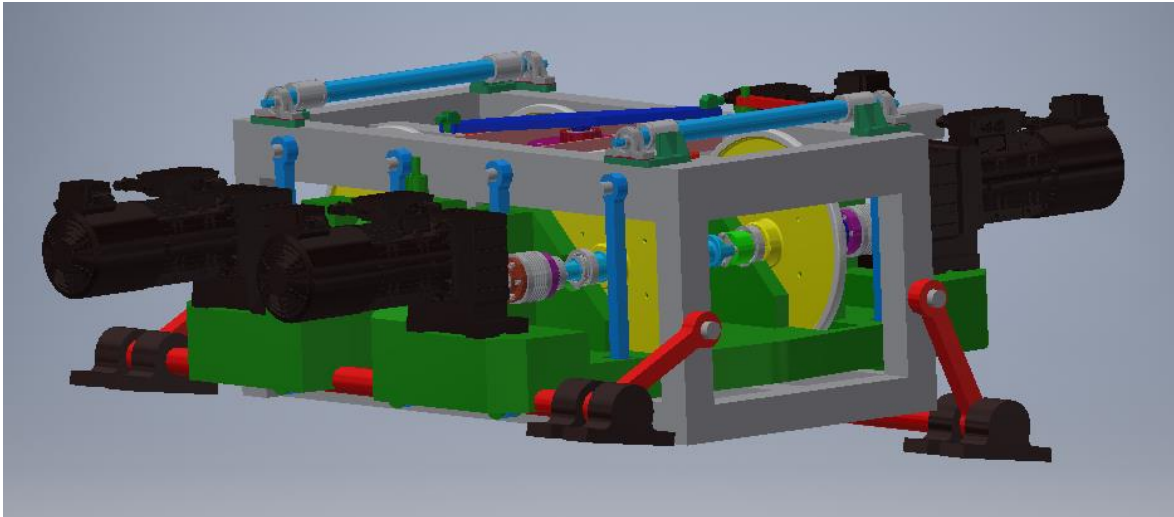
Zobrazení osy rotace v zadaném modelu
